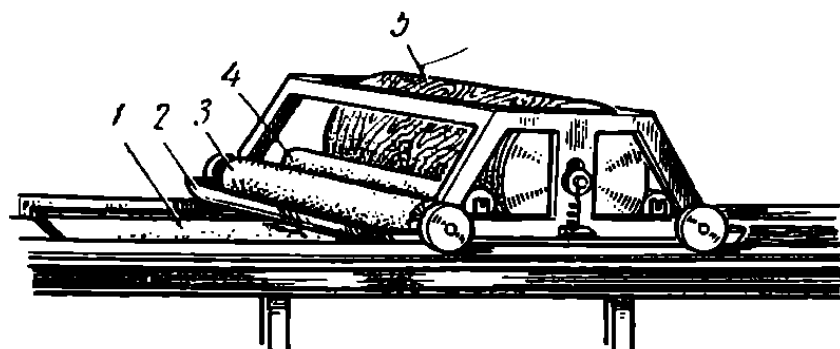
Приспособление для имитации текстуры древесины ценных пород накаткой с кожаного валика
